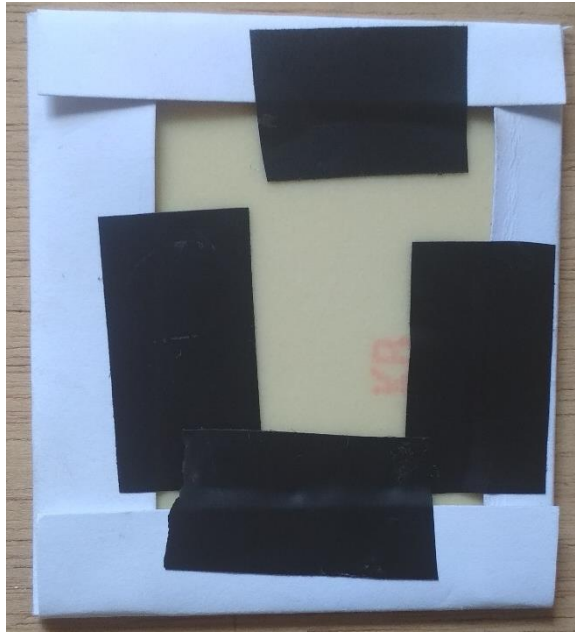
Impresión del circuito diseñado en Eagle PCB. Elaborado por el autor.
